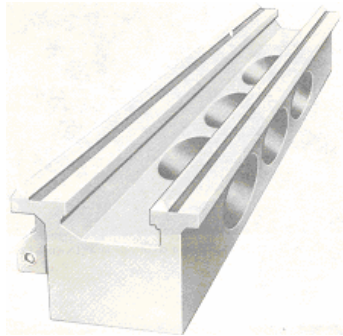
Bancada de un torno (Cortesía de Clausing Corporation).
